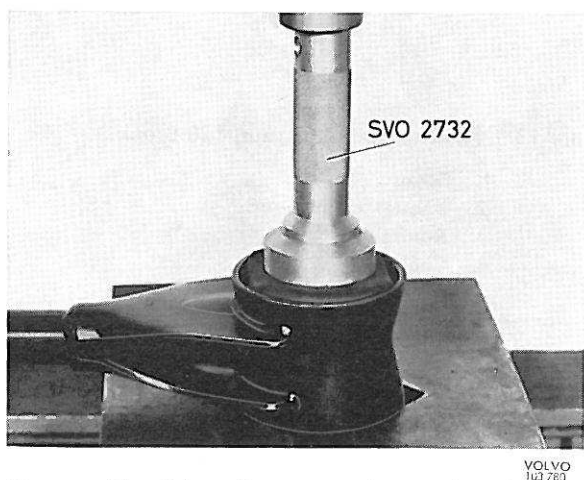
Démontage-remontage des bagues arrière des barres de torsion, 120 et 1800 de nouveau modèle
